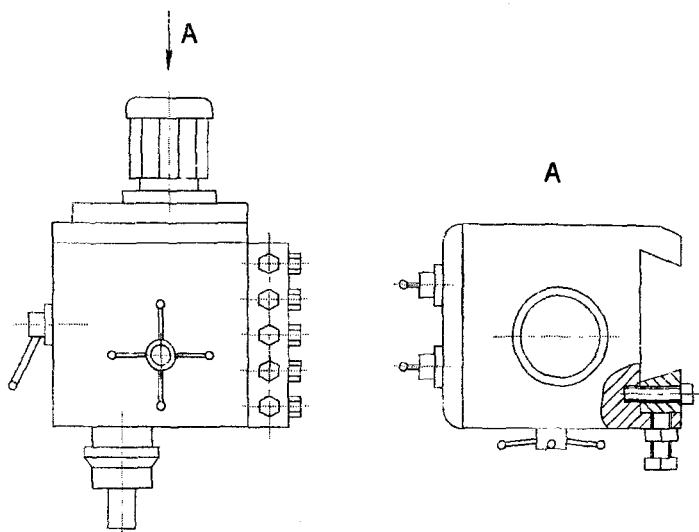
Компоновка шпиндельной бабки вертикально-сверлильного станка
